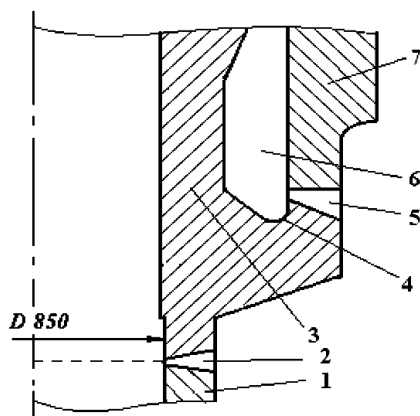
Фрагмент конструкции узла приварки горячего коллектора к корпусу ПГ: 1 – главный циркуляционный трубопровод; 2 – сварной шов; 3 – коллектор; 4 – галтель; 5 – сварной шов № 111; 6 – карман; 7 – патрубок.
